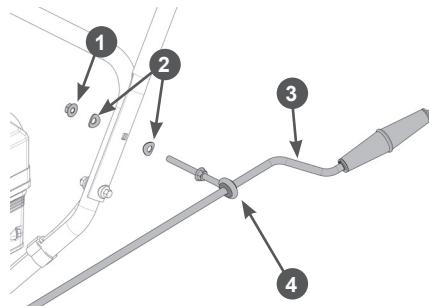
Установка рычага управления поворотом жёлоба (сторона рукояток)
